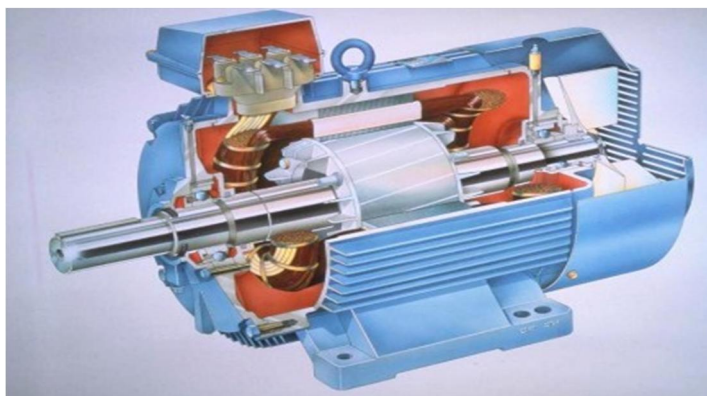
Vue en coupe d'un moteur asynchrone.
